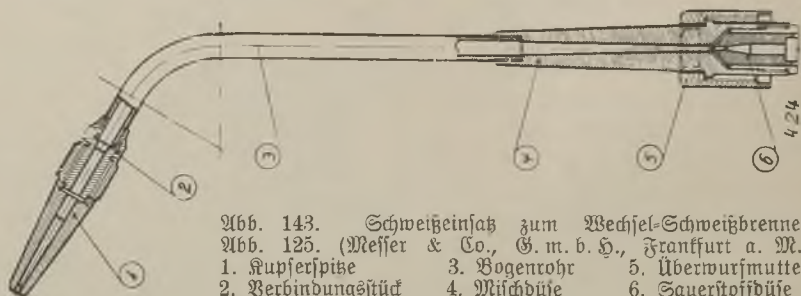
Schweißeinfaß zum Wechsel-Schweißbrenner
